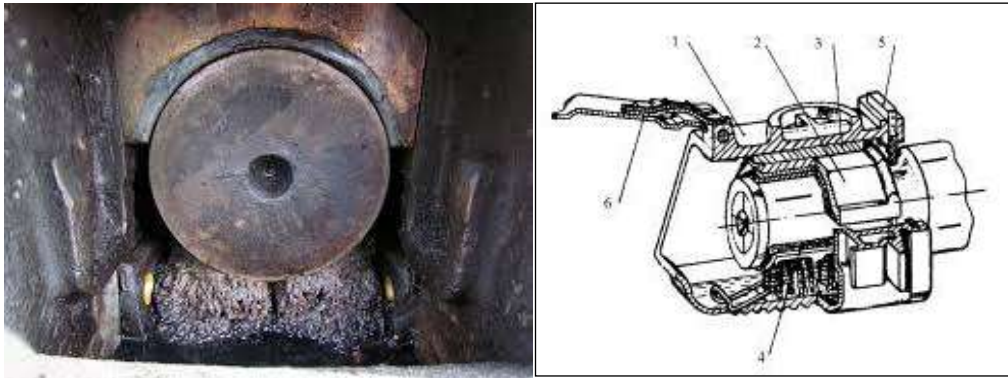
Diseño de una caja de eje con cojinete de fricción [3].
